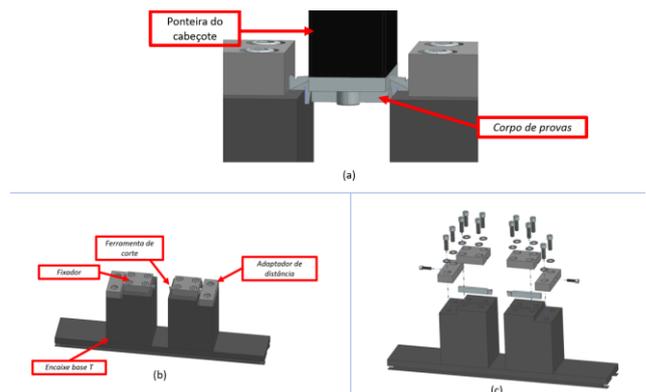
(a) layout do dispositivo, (b) detalhe do dispositivo e (c) vista explodida do dispositivo
